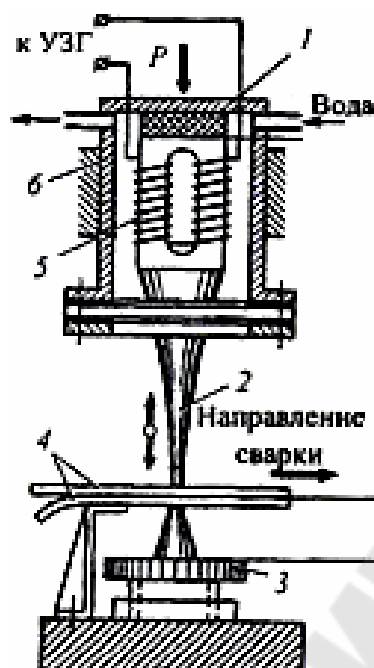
Схема ультразвуковой сварки: 1 — акустический узел; 2 — инструмент (волновод); 3 — регулировочный винт опоры; 4 — свариваемые детали; 5 — вибратор; 6 — кожух
